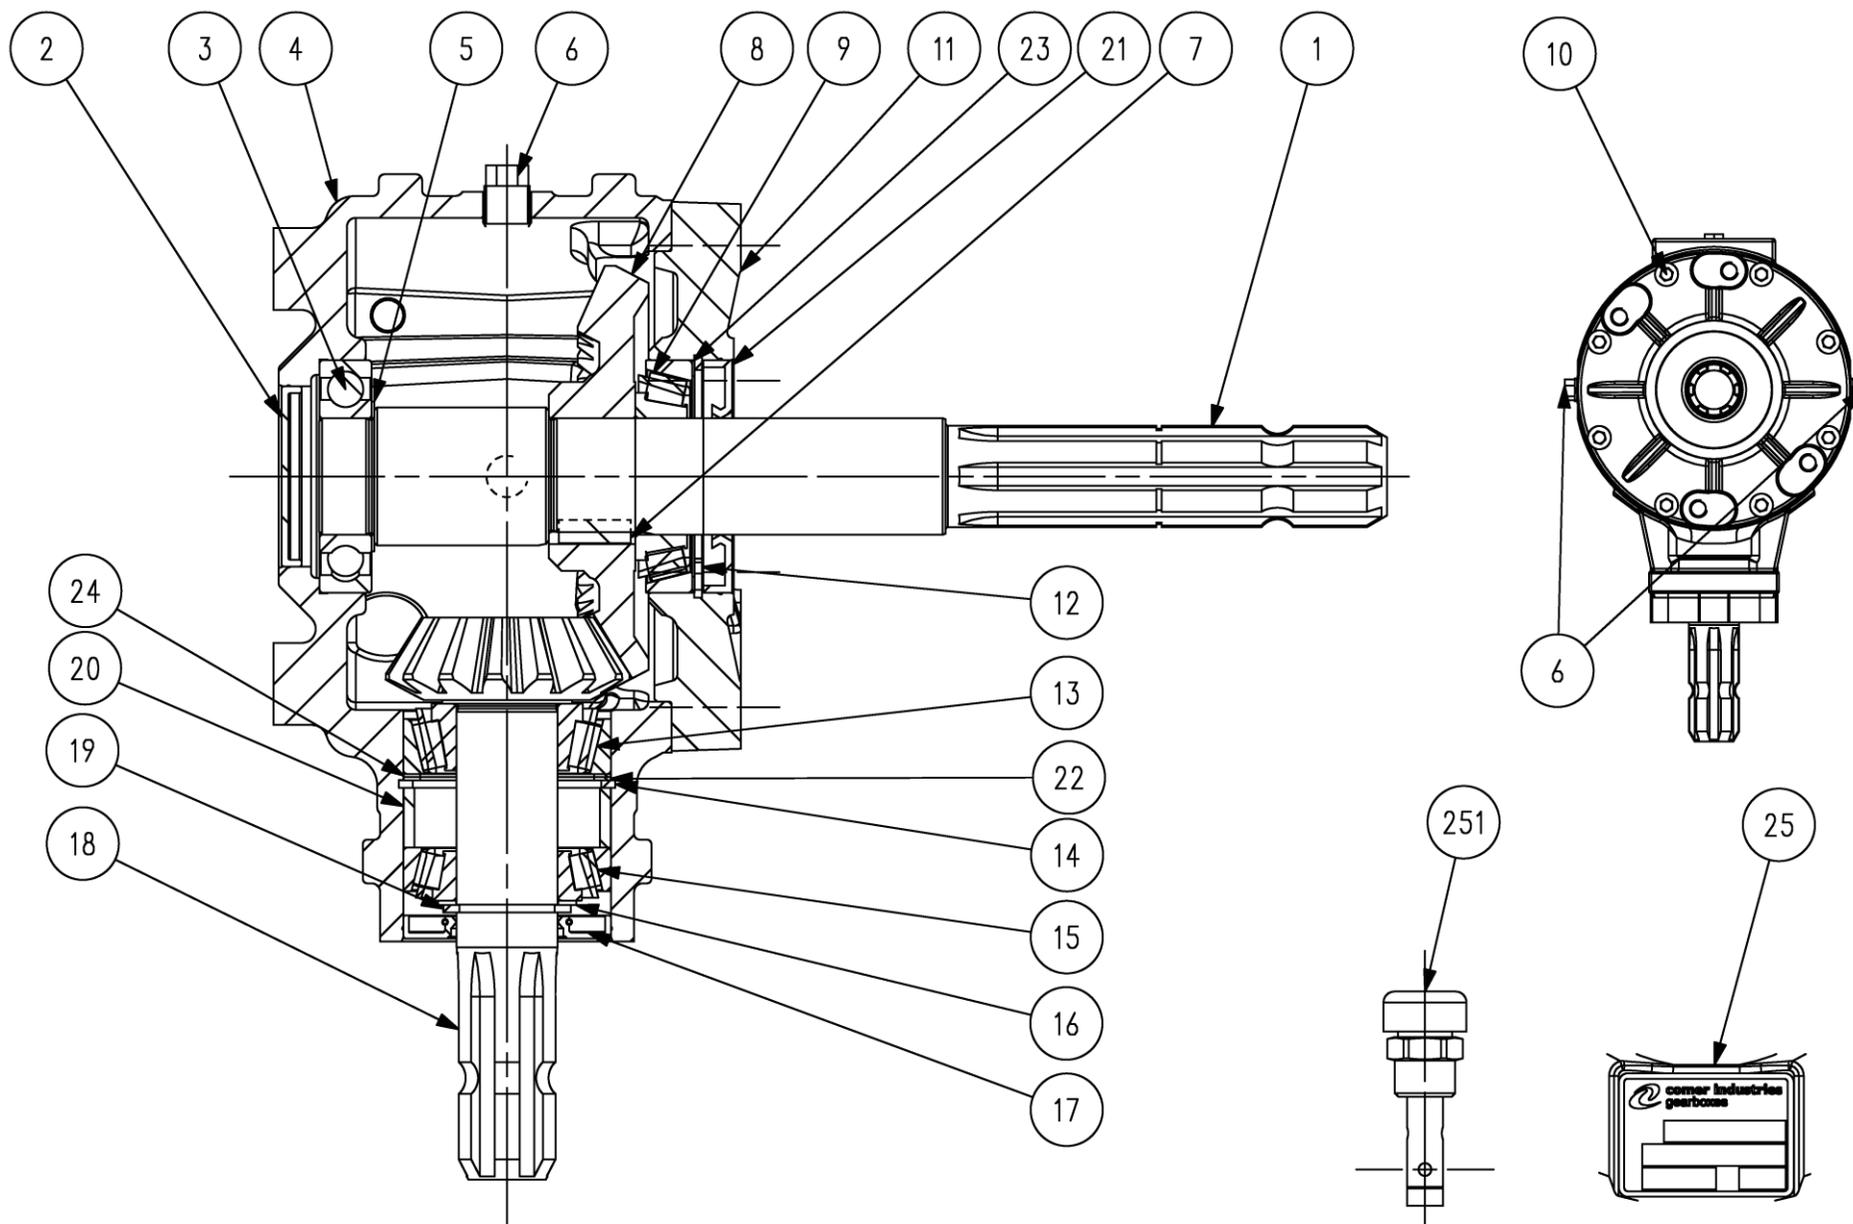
Редуктор 9.304.528.00 "Comer industries"
